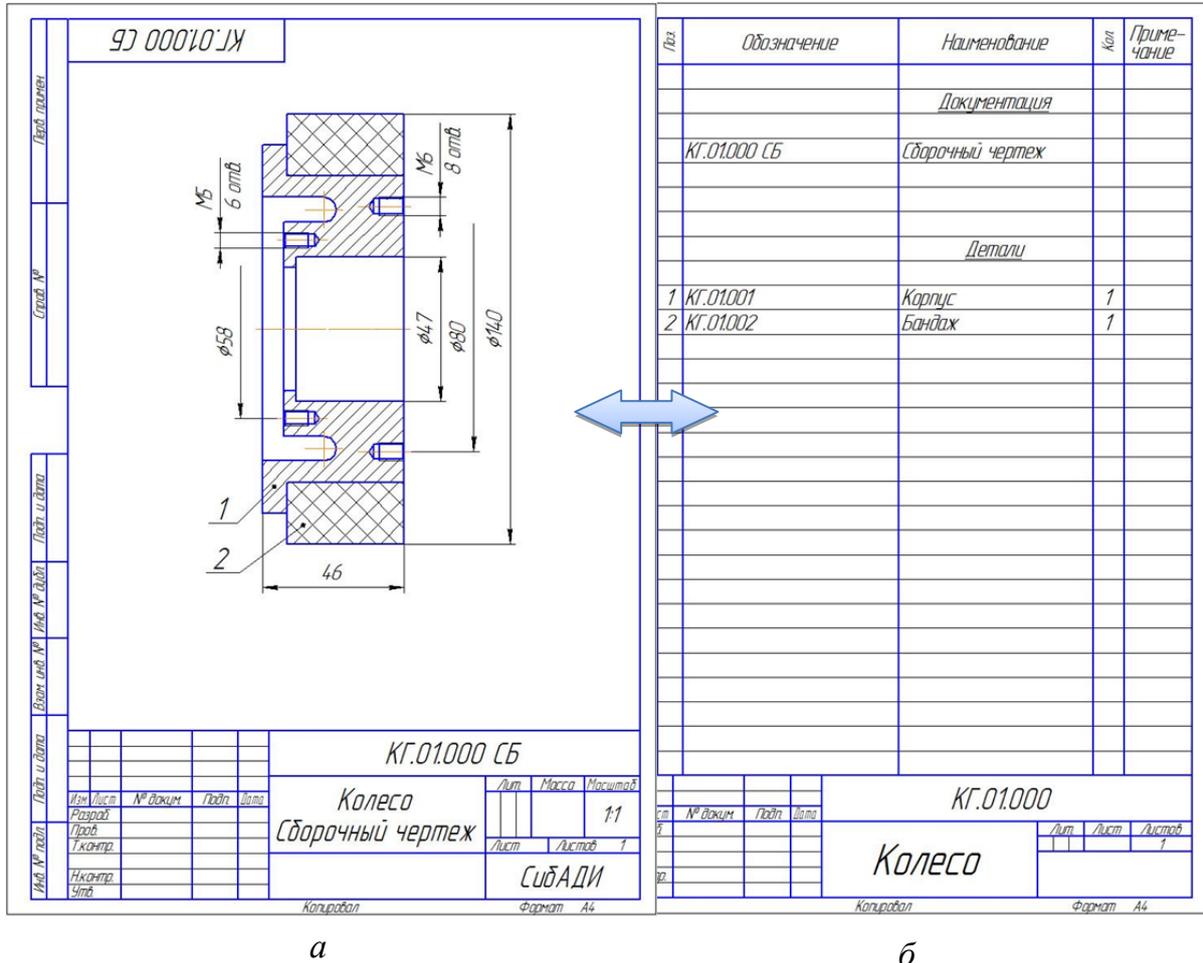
Сборочный чертеж сборочной единицы «Колесо»:
